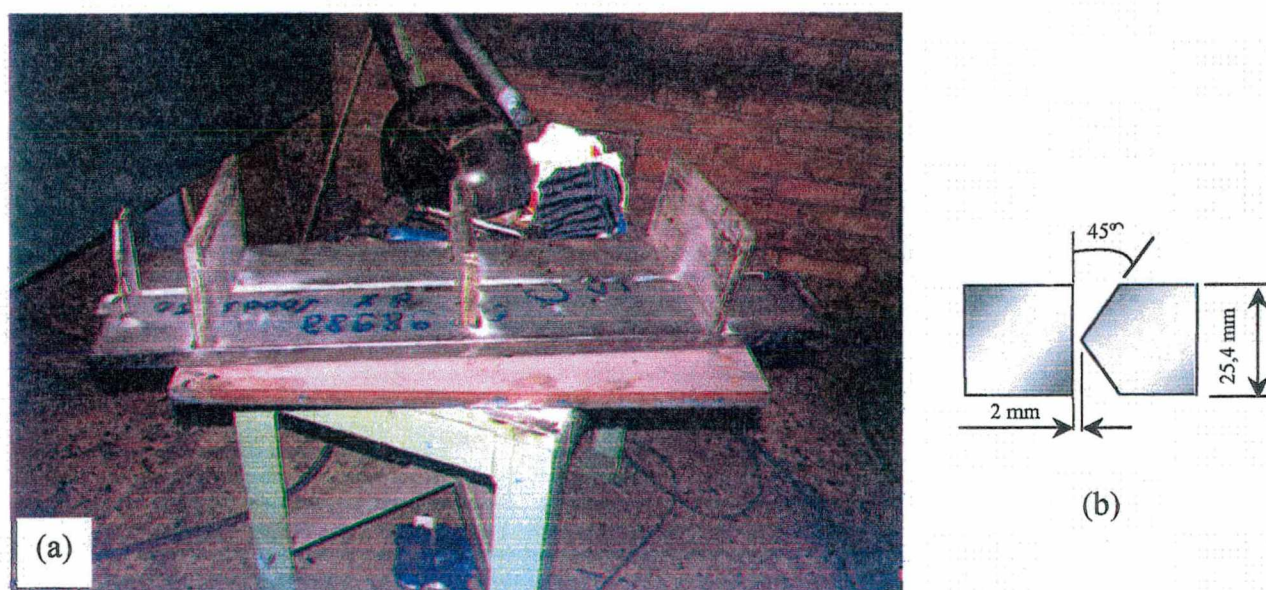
Detalhe da soldagem. (a) Restrições para soldagem da chapa de do aço inoxidável duplex UNS S31803; (b) Detalhe do chanfro em “K”.
